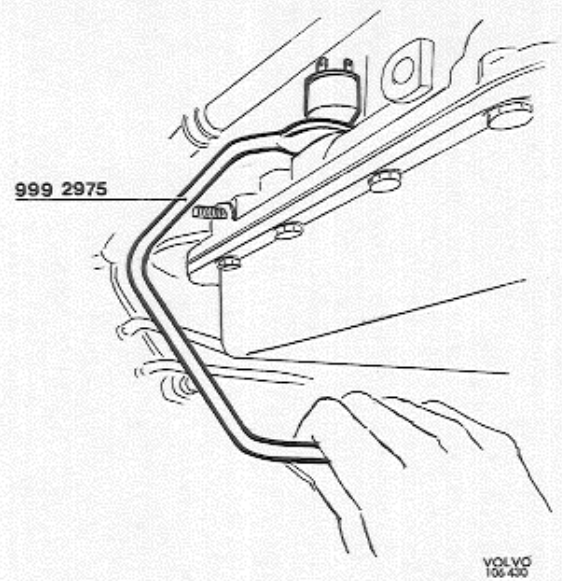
7 Spezialschlüssel für Gegenmutter der Anlaßsperre
